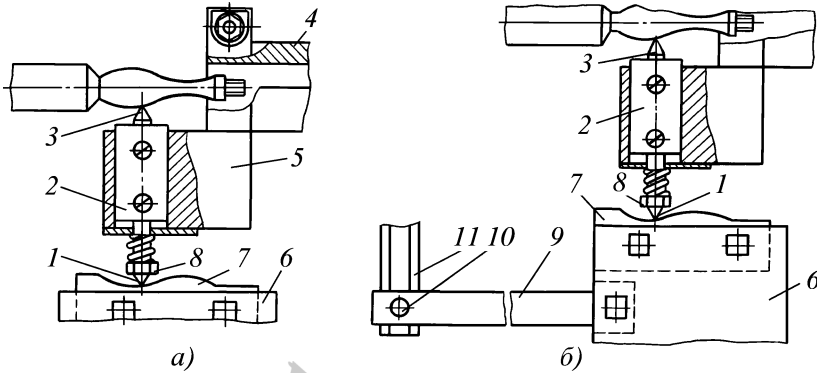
Приспособление для обточки фасонных поверхностей:
